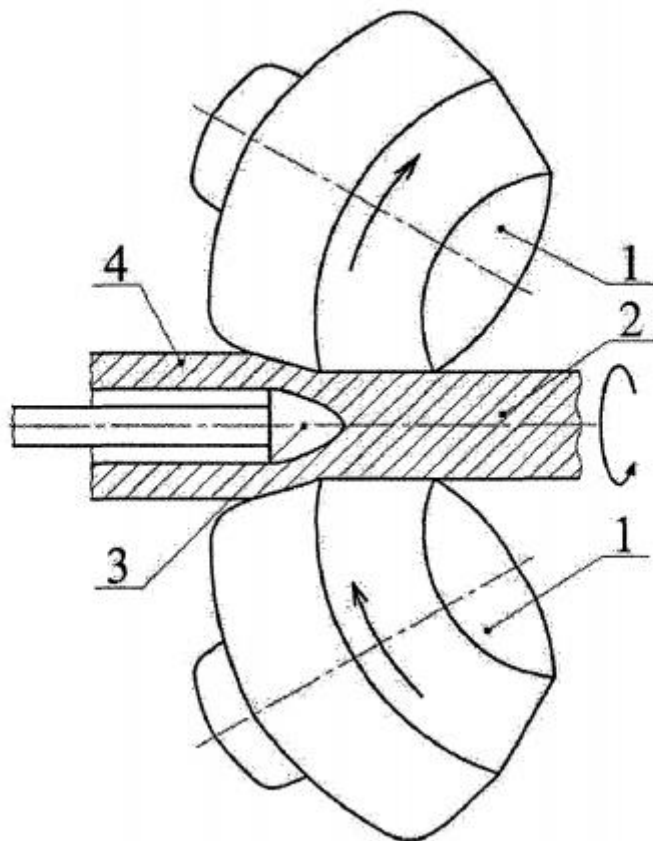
Схема процесса прошивки в стане с грибовидными валками: 1 – валки; 2 – заготовка; 3 – оправка; 4 – гильза
